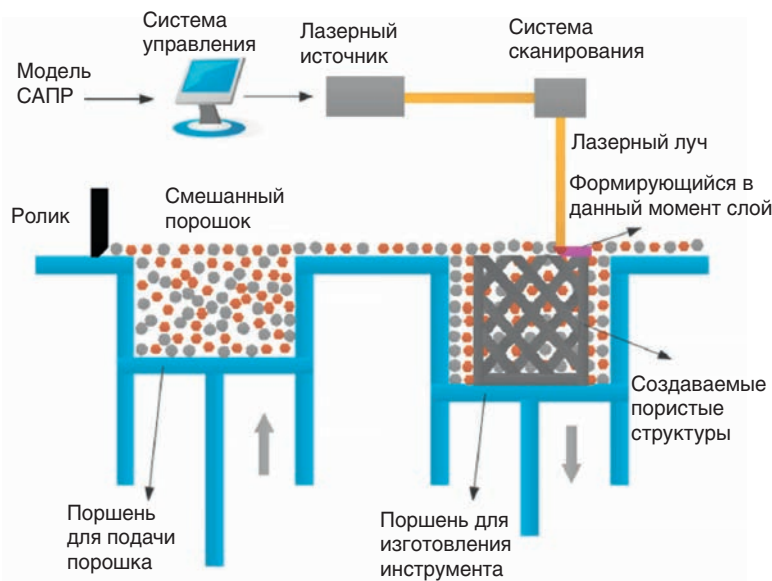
Схема установки для изготовления шлифовальных кругов пористой структуры на металлической связке с использованием SLM-процесса
